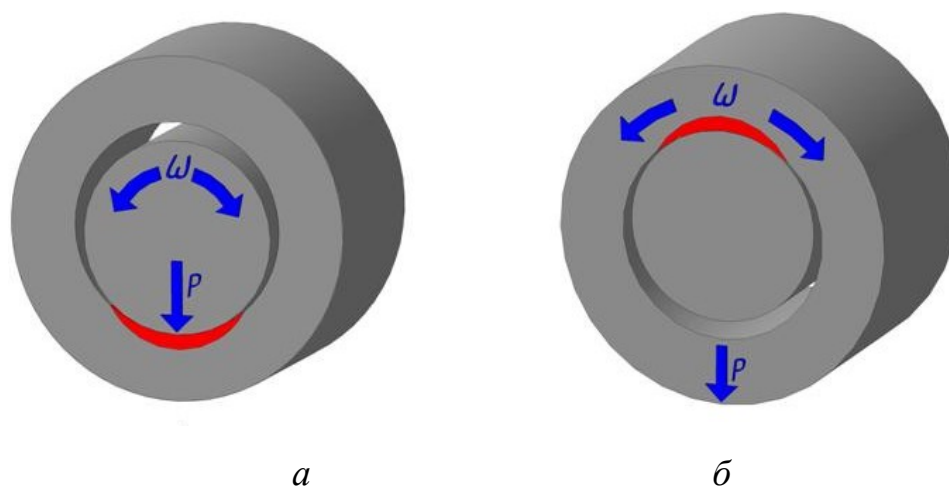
Схемы контактного взаимодействия деталей гладких цилиндрических подвижных соединений: *а* - опорное отверстие и подвижный вал; *б* - опорный вал и деталь с отверстием, опирающаяся на вал
